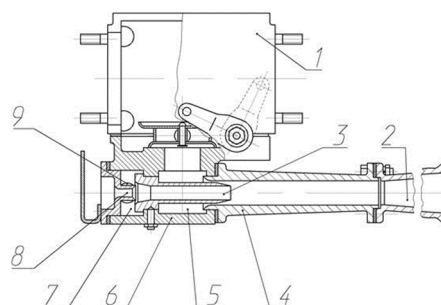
Двухступенчатый вакуумный насос: 1 – корпус распределительной камеры; 2 – диффузор; 3 – промежуточное сопло; 4 – приемное сопло; 5 – промежуточная камера, 6 – корпус, 7 – камера разрежения; 8 – воздушное сопло; 9 – отверстие для подключения трубопровода вакуумной
